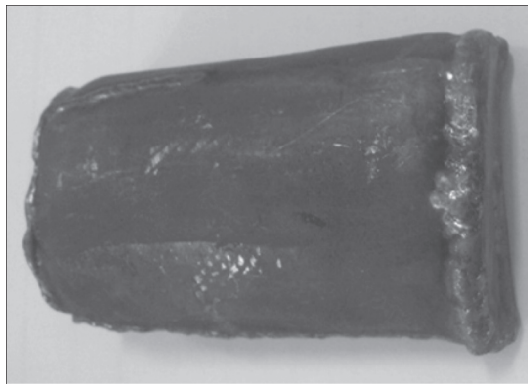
Зразок інтерметалідного сплаву, запакований в оболонку з низьковуглецевої сталі
